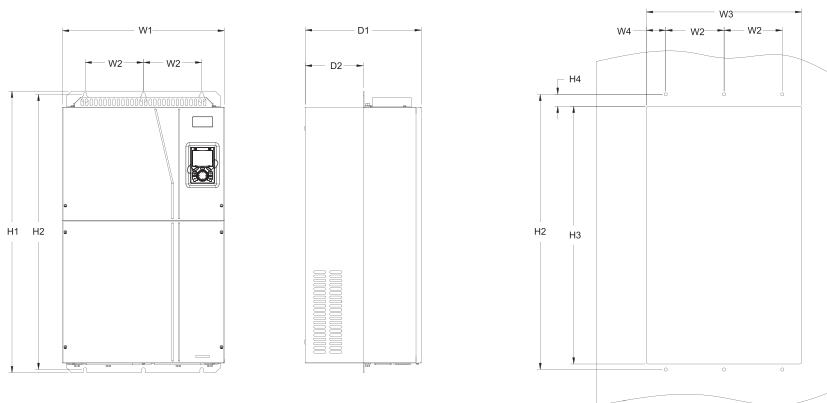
Схема ПЧ фланцевого монтажа 660 В, от 160 кВт до 220 кВт
